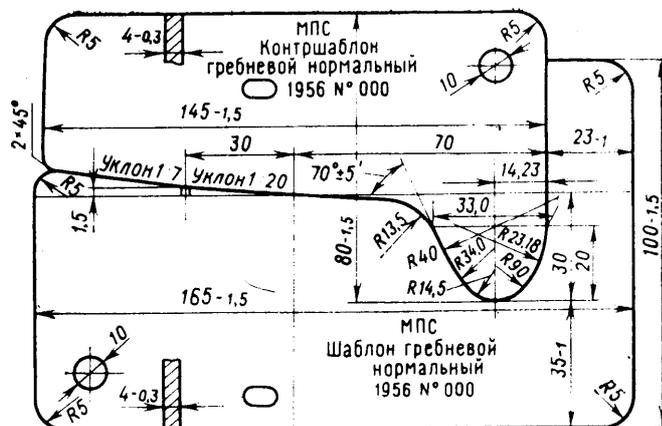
Шаблон и контролшаблон для проверки профиля бандажа колесной пары
